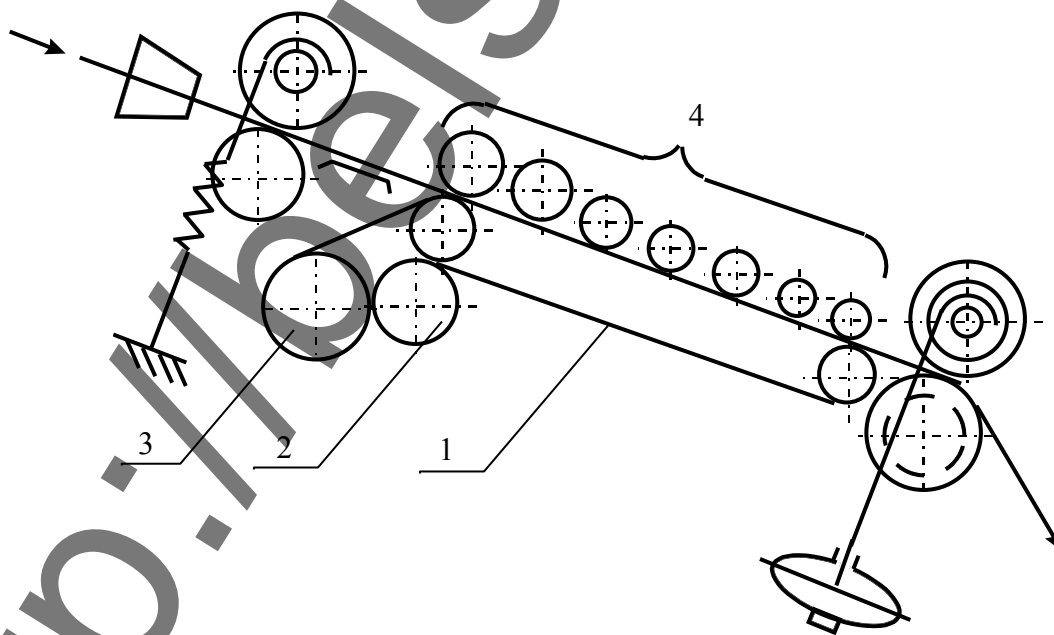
Схема вытяжного однозонного прибора с самогрузными валиками
